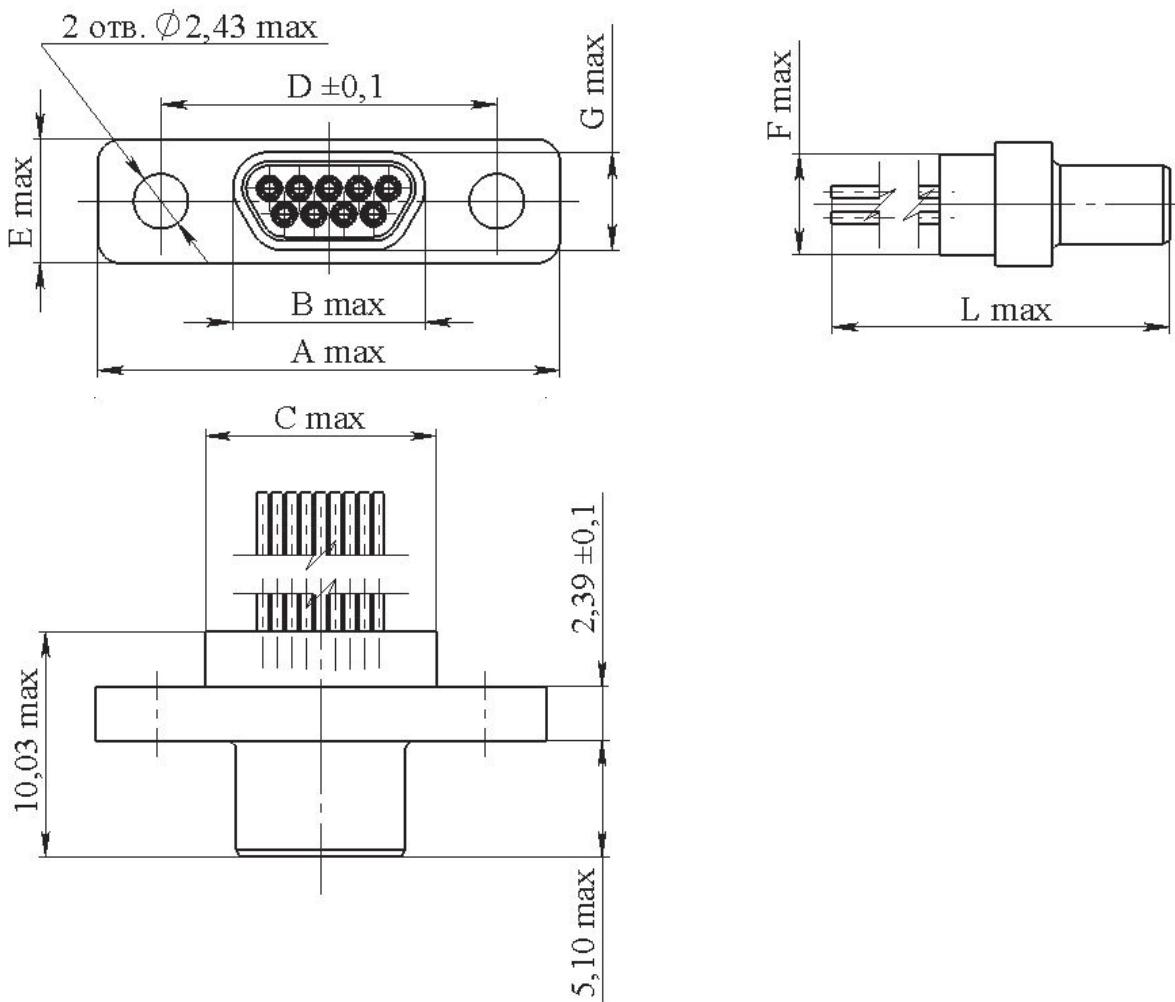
Соединитель СП397-1Р...Ш213(4)
